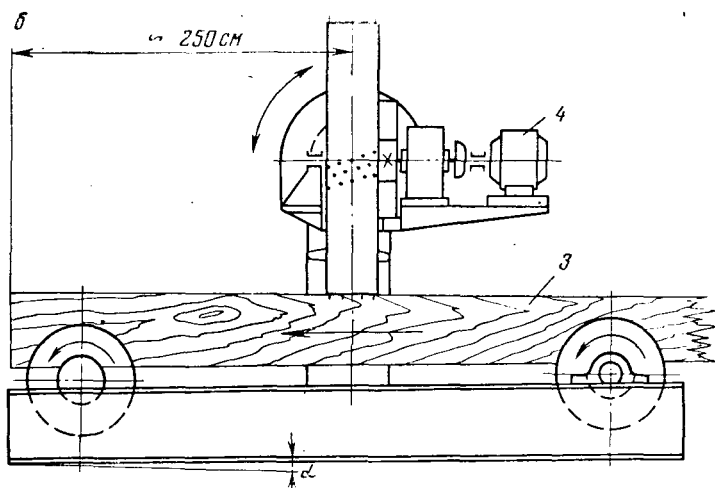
Схема станка ЦНИИС для накалывания бревен:
